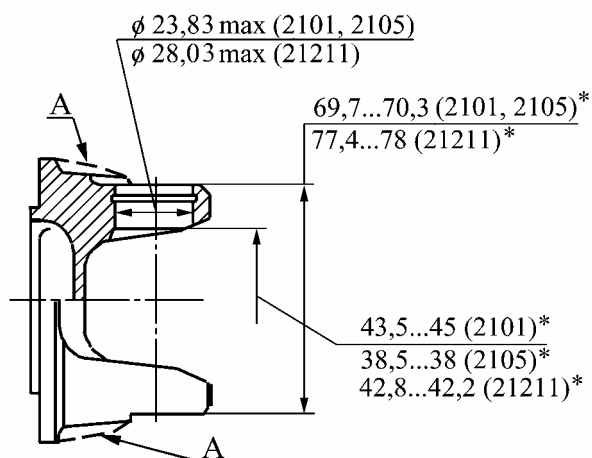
Фланец карданного вала 2101/2105/21211-2201023.
